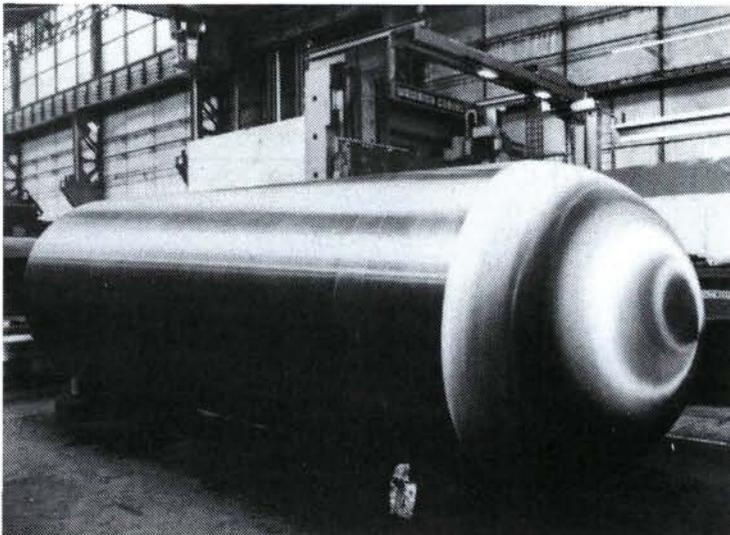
Vasija fabricada con soldadura con cambio de dirección (shape welded).
